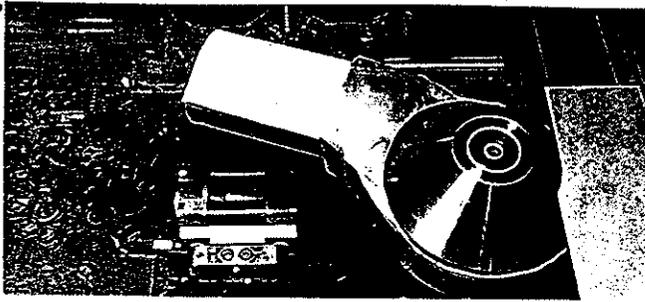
Versuchswerkzeug mit innenliegender Spanabführung
